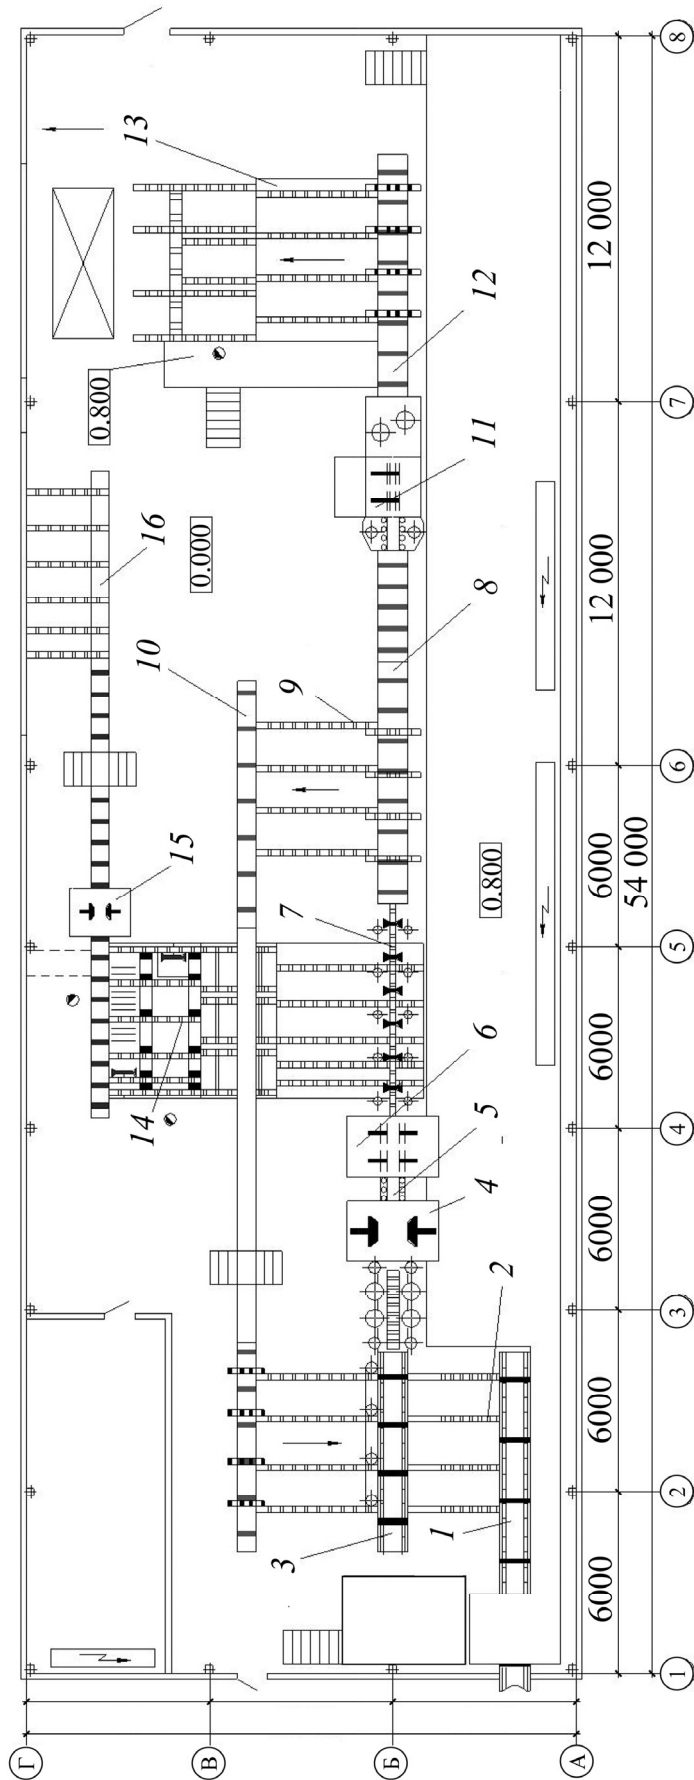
Схема лесопильного цеха на базе фрезернопильного оборудования с рециркуляцией брусков:
